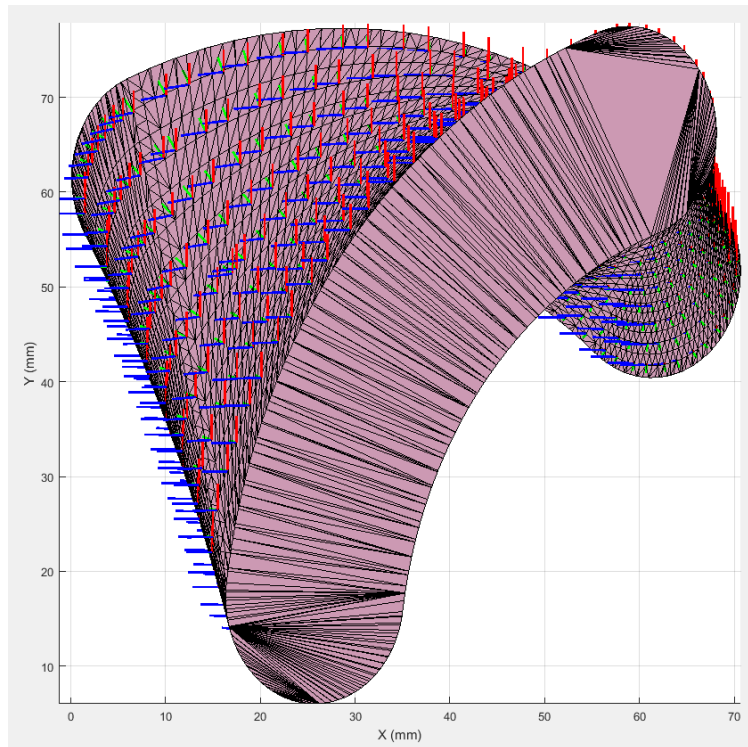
Vista de planta de la pieza con los sistemas de coordenadas de los puntos del perímetro.
